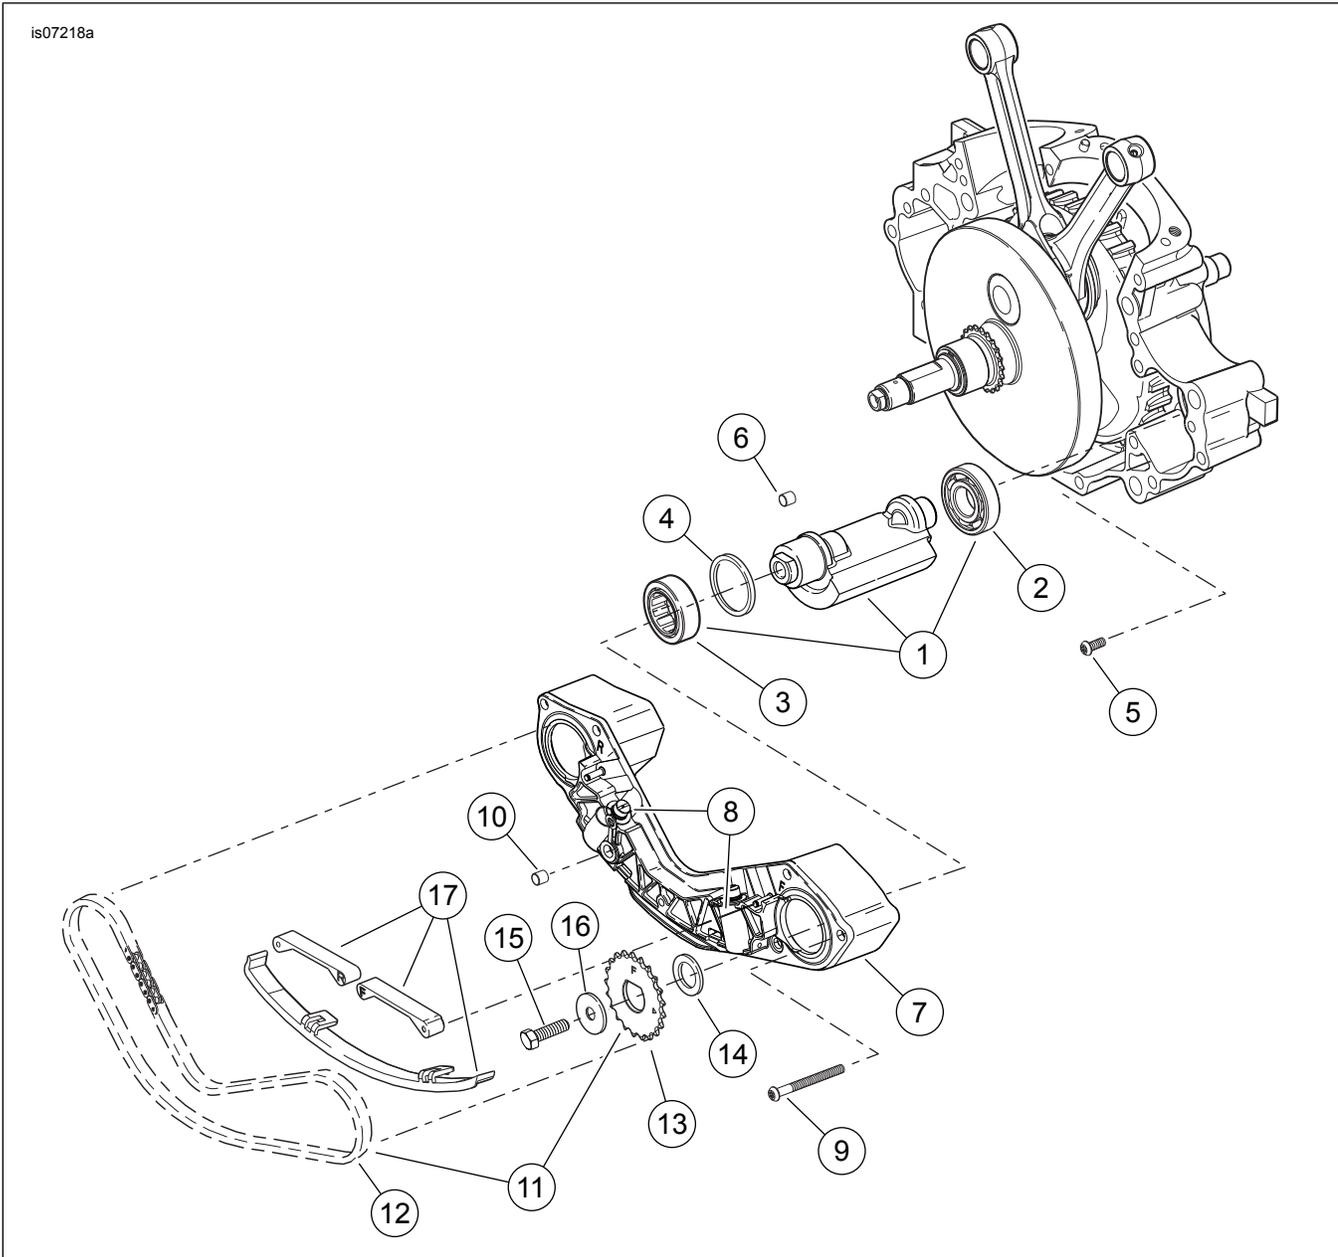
Piezas de servicio: Compensador del motor ensamblado Screamin' Eagle Pro SE120R (Beta)
